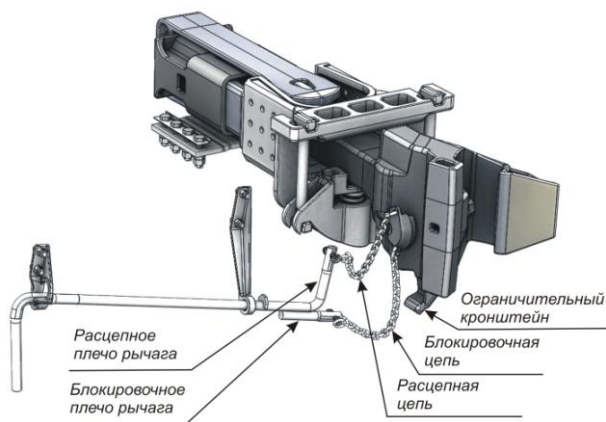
Расцепной привод автосцепки СА-3 с блокировочной цепью
